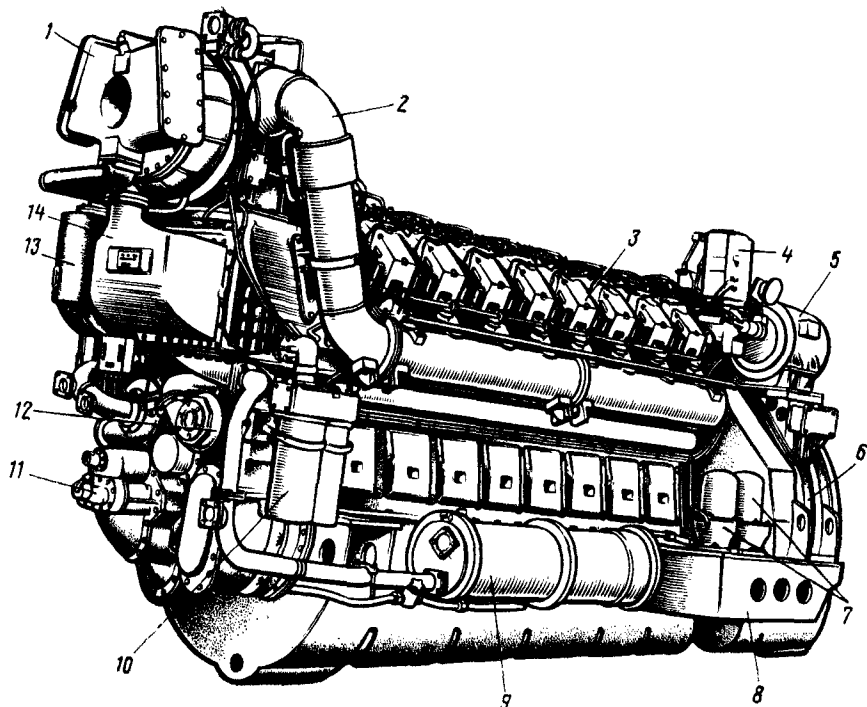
Внешний вид дизель-генератора 2А-9ДГ:
